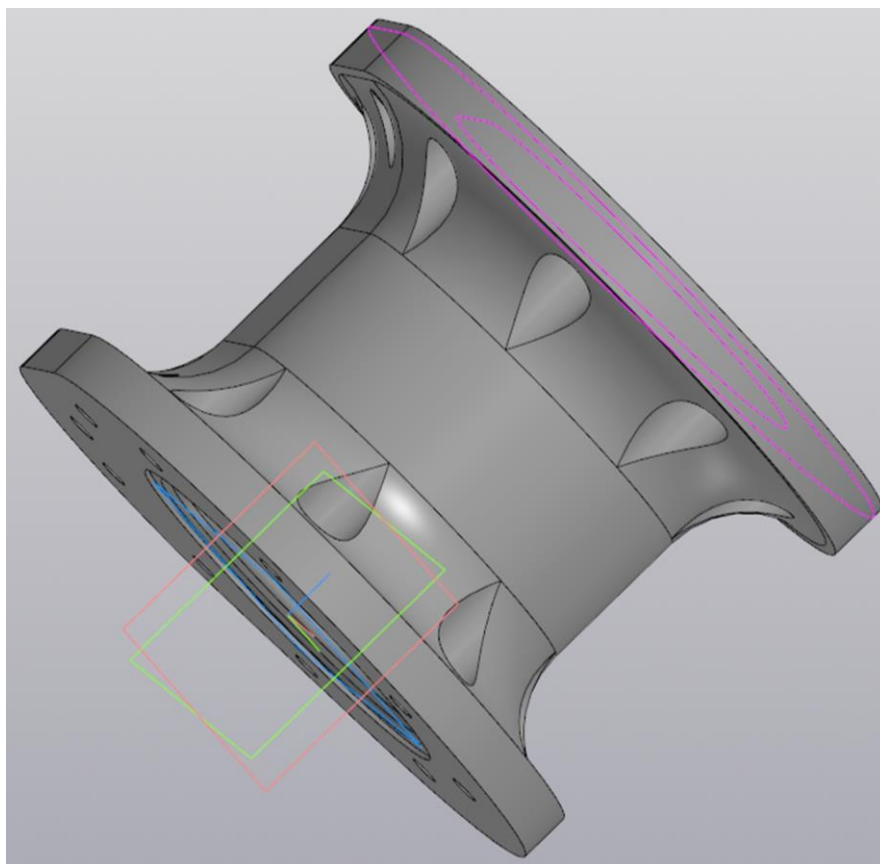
Модернизированная верхняя часть корпуса редуктора
